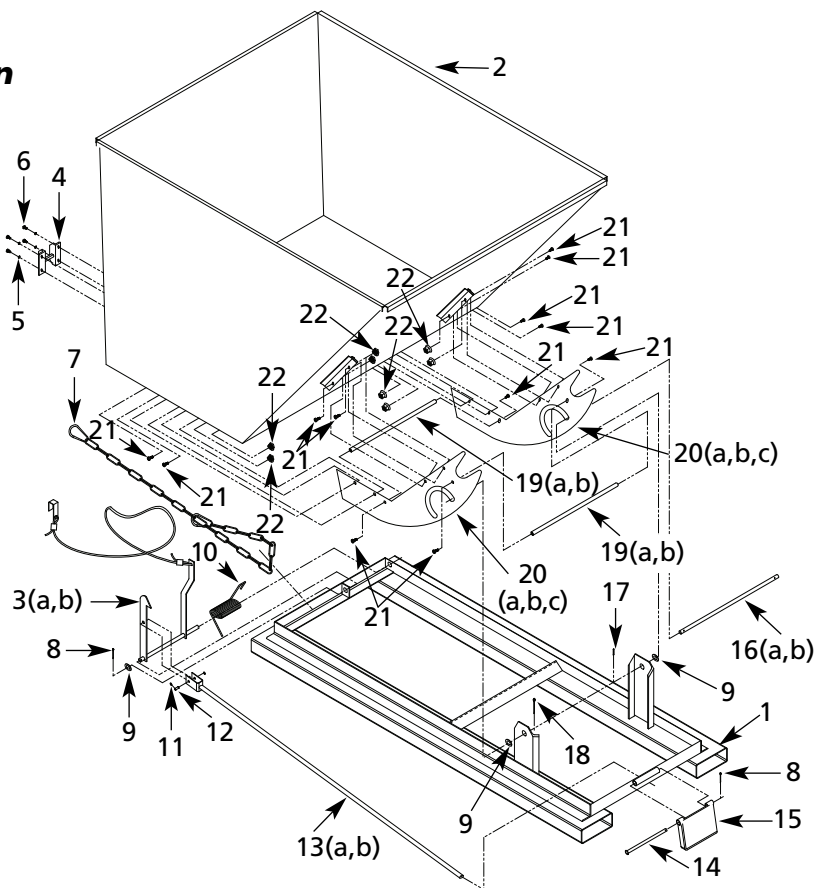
Illustration des pièces détachées pour les bennes à déclenchement frontal
